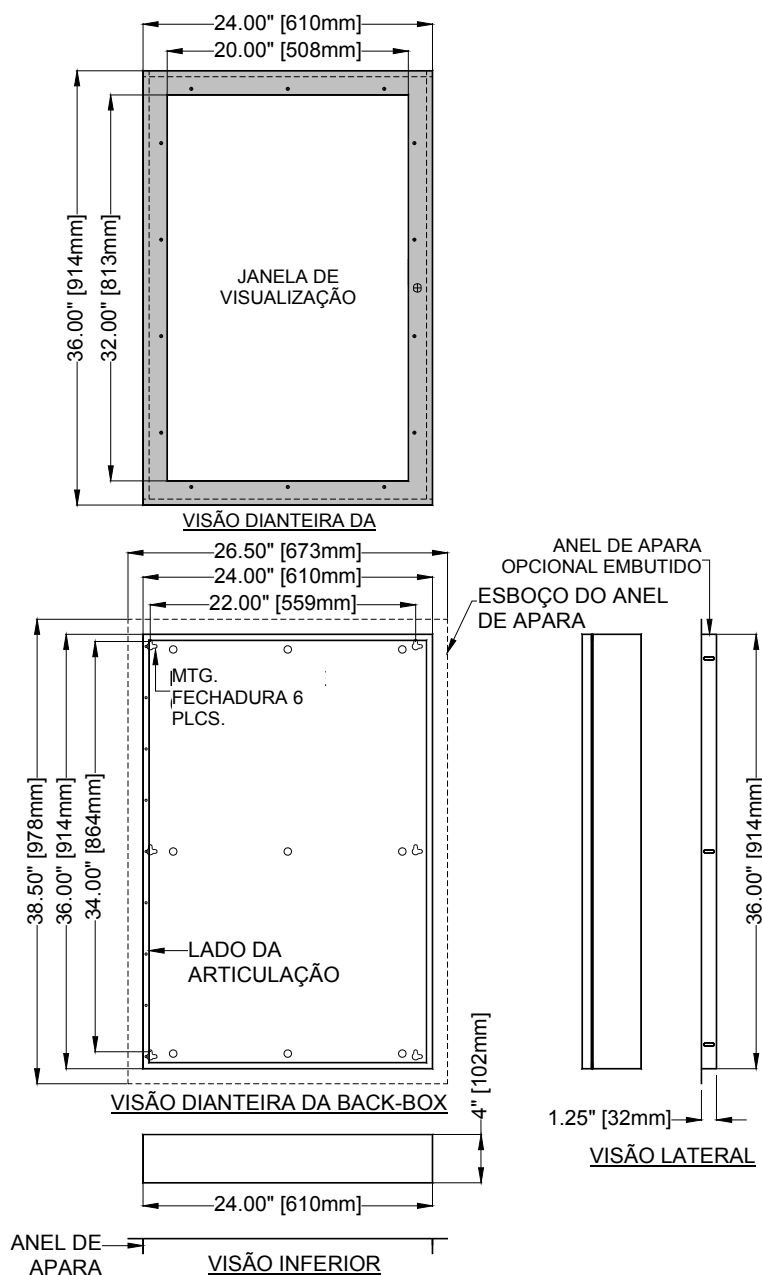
10-123 Dimensões do conjunto de portas e da back-box
